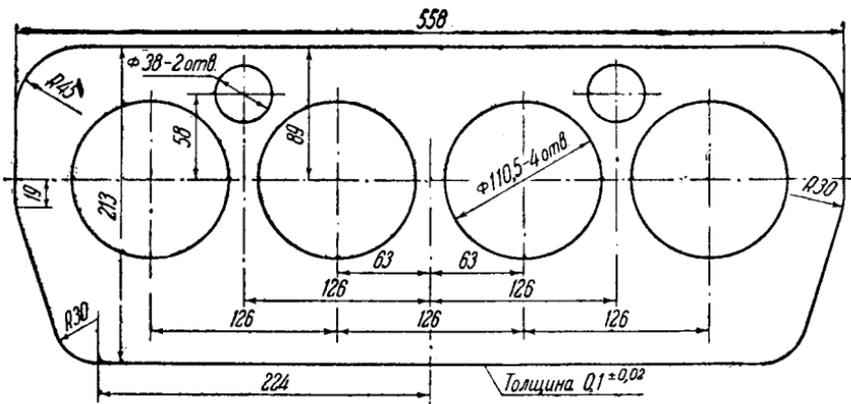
Дет. № 02-04. Лист верхний прокладки головки цилиндров
